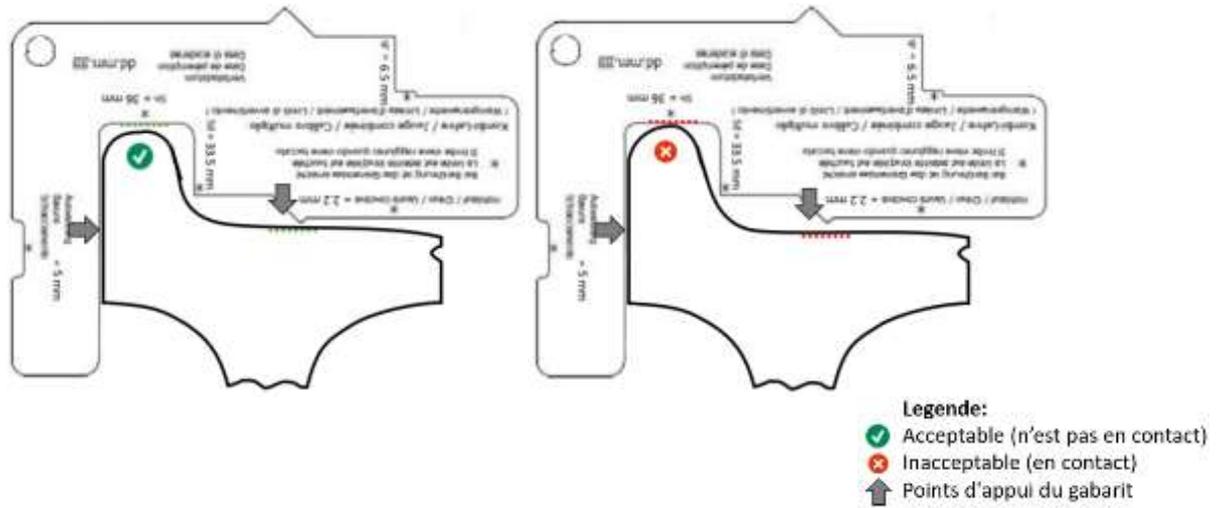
Largeur du boudin de roue (Mesure Sd)
